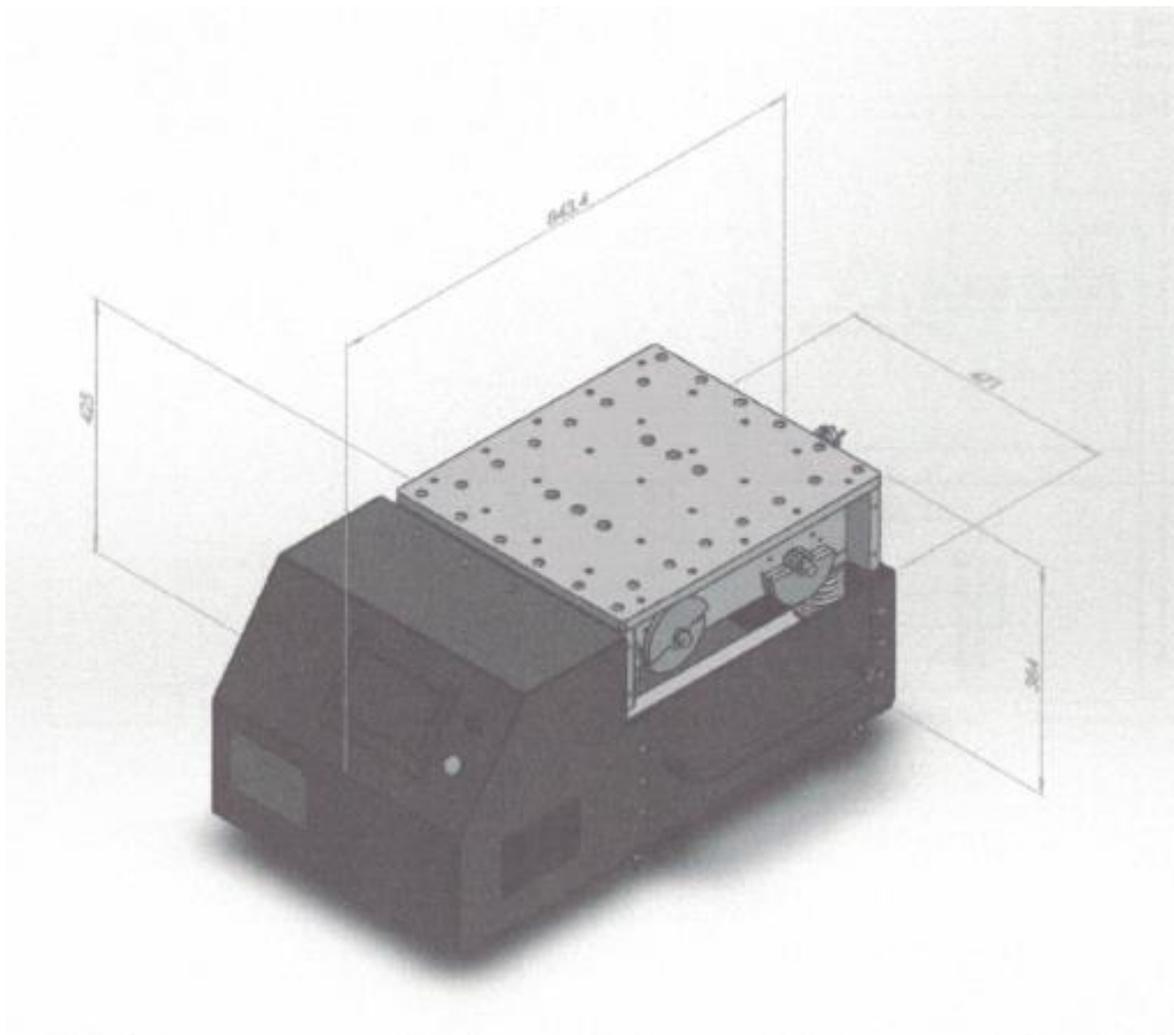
Внешний вид вибростенды с основными размерами
